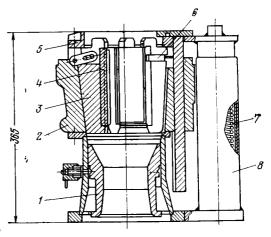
Спайдер АСГ-80: I — вкладыш пентратора; 2 — корпус; 3 — корпус клина; 4 — плашка; 5 — подвеска; 6 — синхронизатор клина; 7 — пружина ползуна; 8 — направляющая
